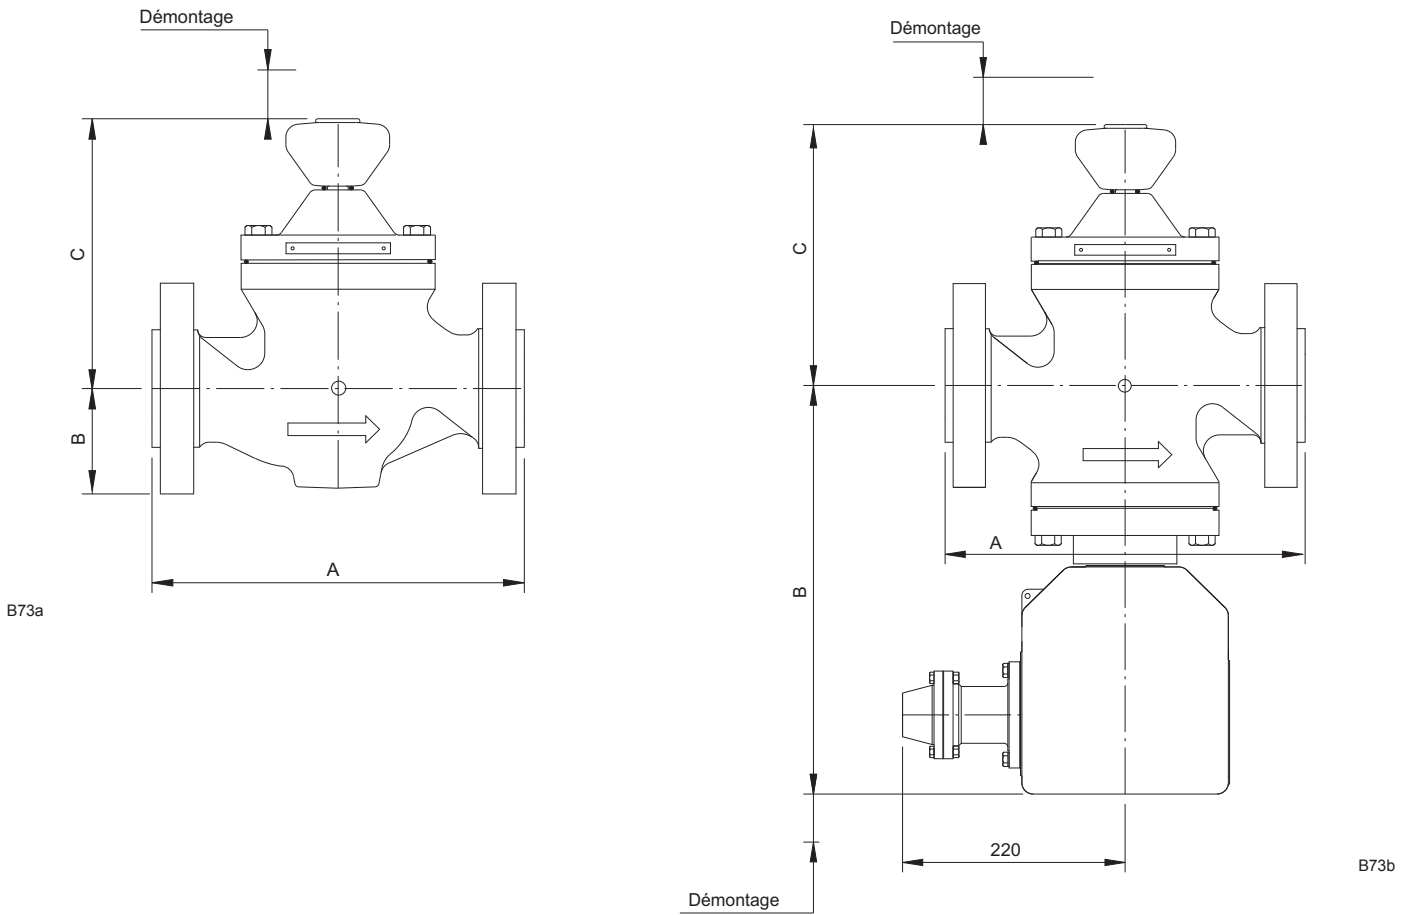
Dimensions des Vannes de Laminage Types BLE et BLX
